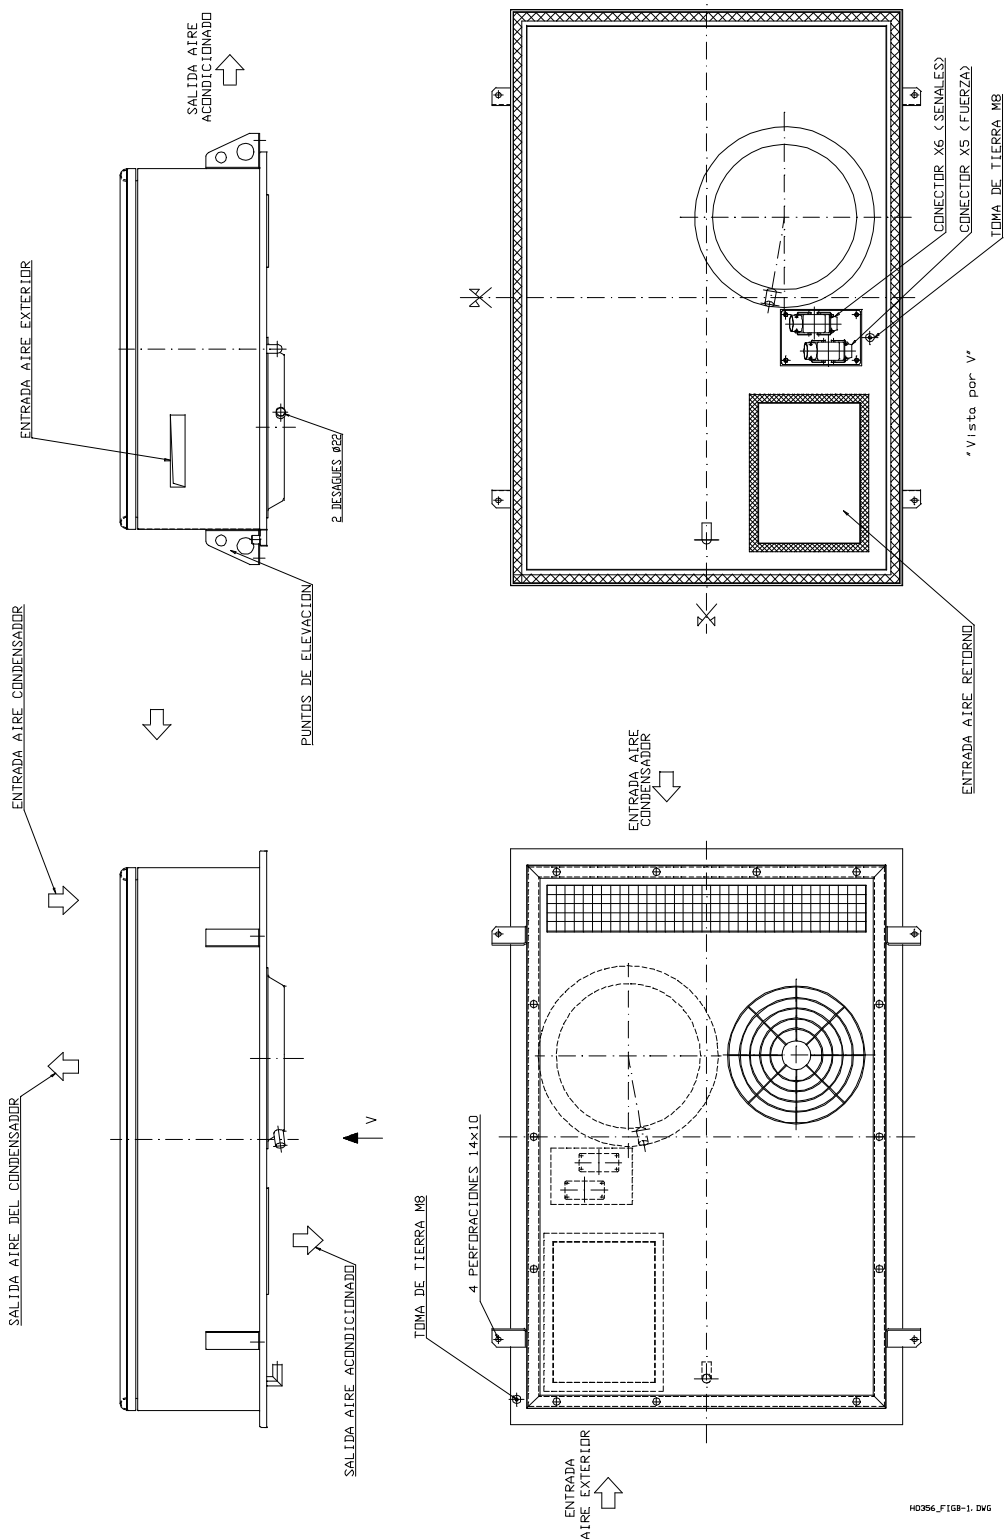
Desmontaje y Montaje del Equipo de A.A. de Cabina RP-4.2
